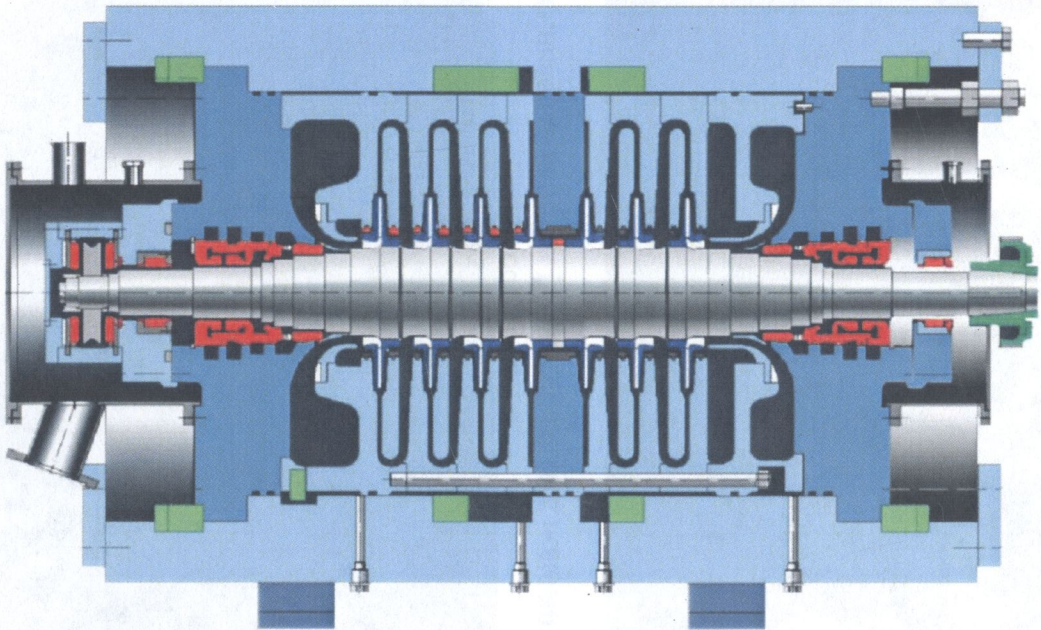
Поздовжній розріз компресора з корпусом типу «барель» (без горизонтального рознімання)
